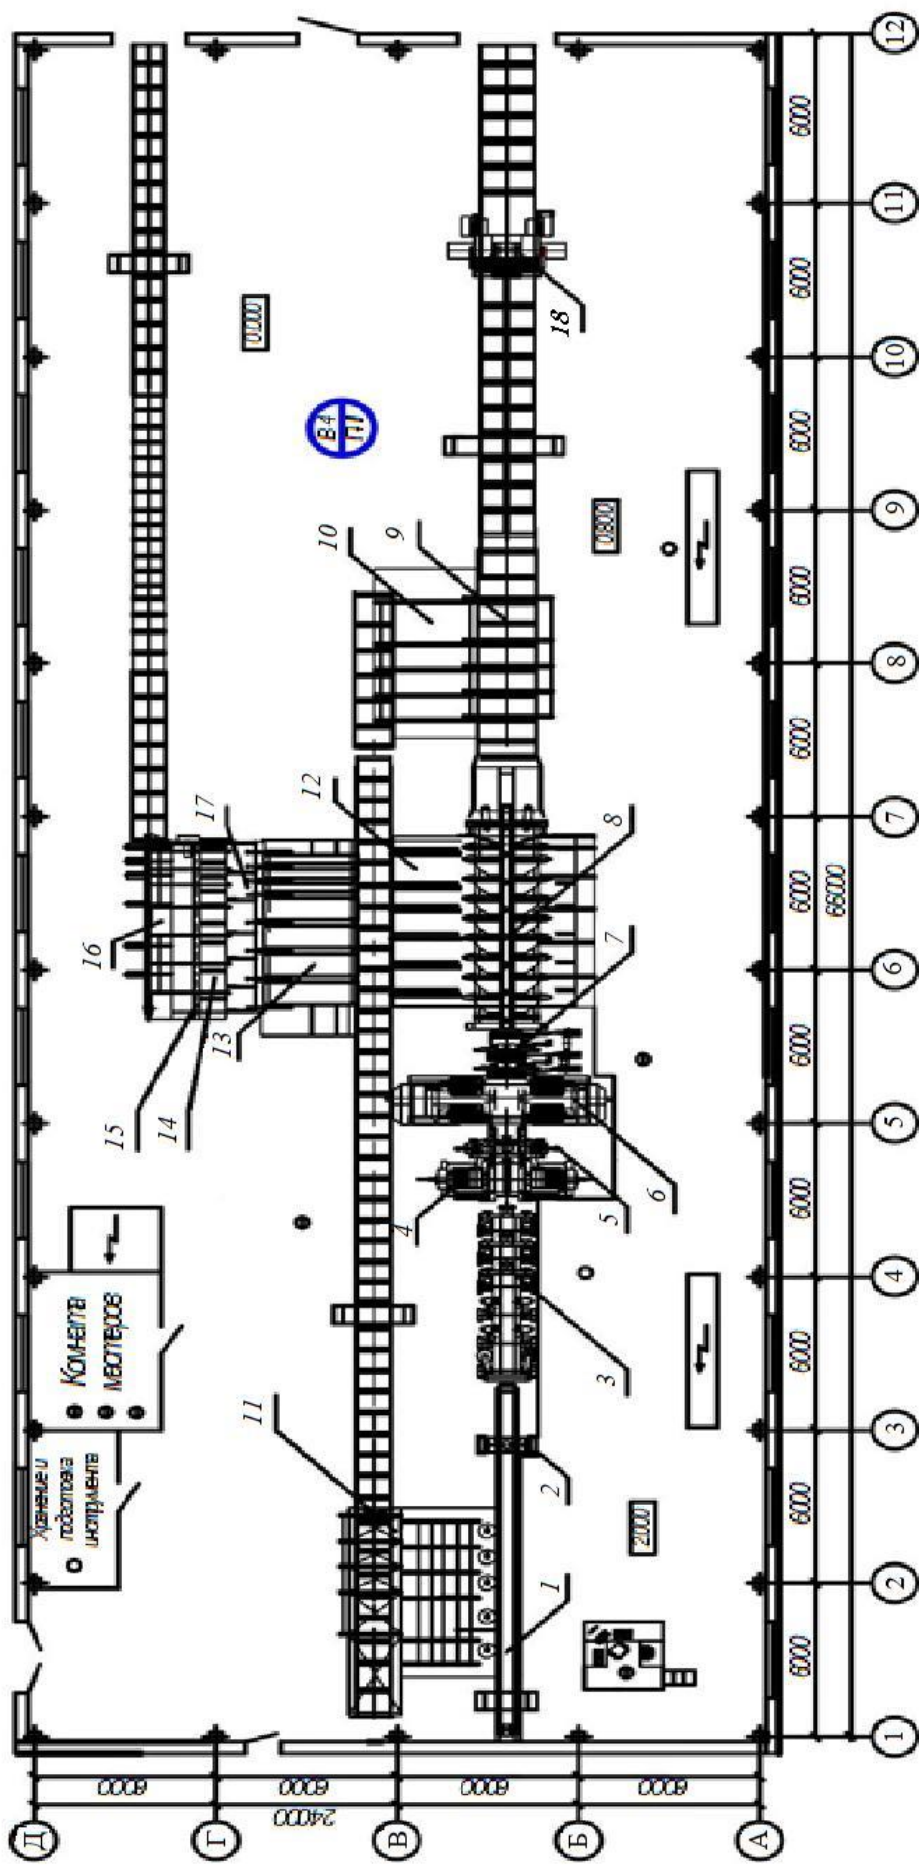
Схема цеха на базе фрезерно-брусующего и круглопильного оборудования:
